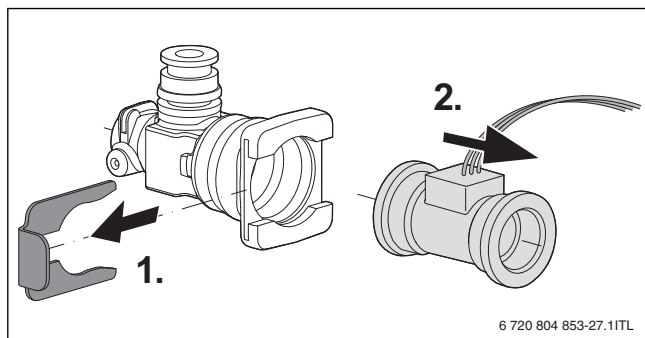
Smontaggio della turbina dal tubo dell'acqua fredda
